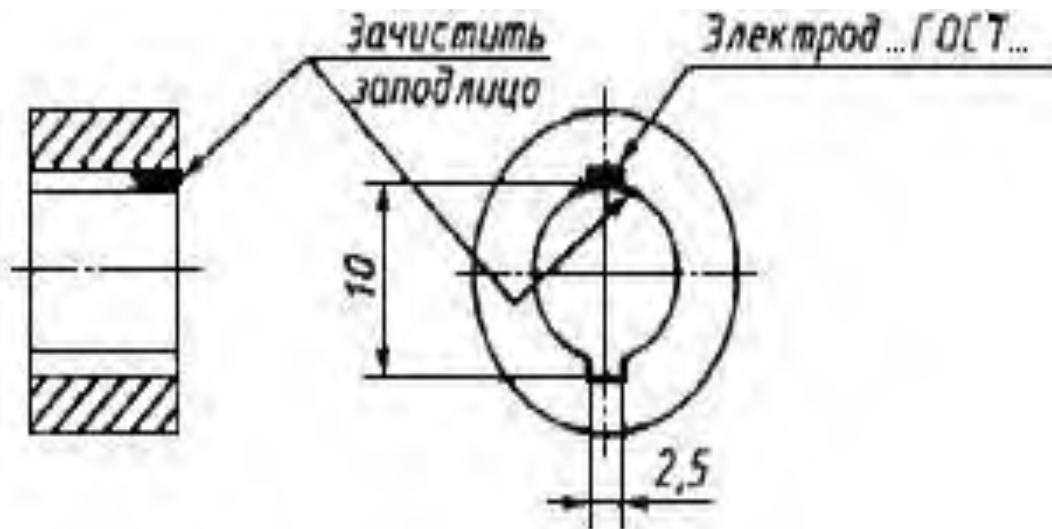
Пример изображения изделия, ремонтируемого наплавкой, заливкой (при помощи сварки, пайки и т.п.)
